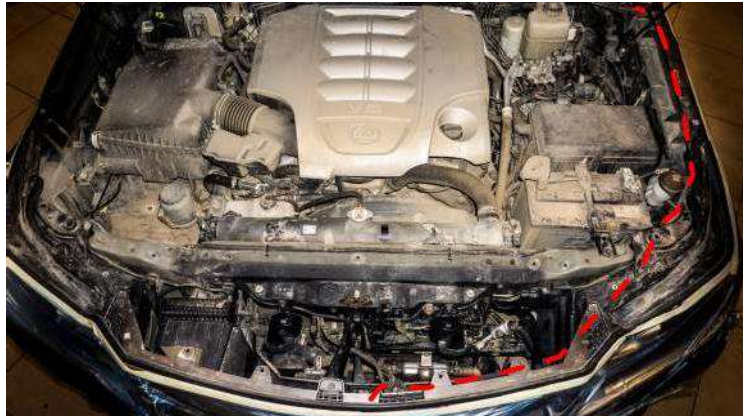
Установка корпуса омывателя и расположение трубки
